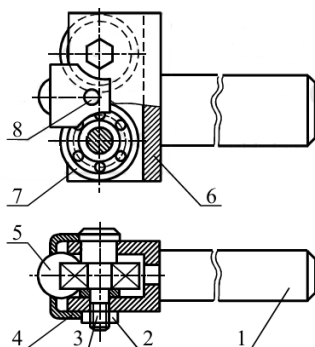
Накатник кульковий: 1 – державка; 2 – гайка; 3 – вісь; 4 – сепаратор; 5 – кулька 6 – корпус; 7 – шарикопідшипник; 8 – гвинт
